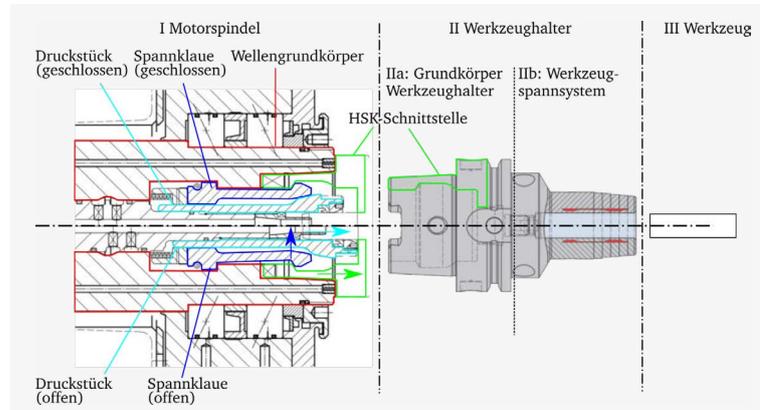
Darstellung des Systems Motorspindel-Werkzeugaufnahme-Werkzeug
